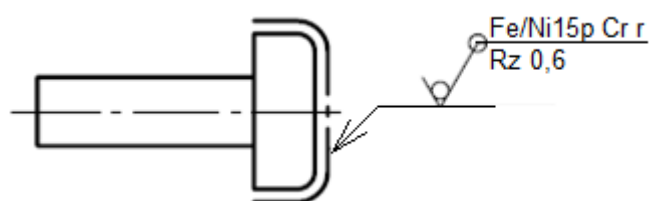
Úprava povrchu špeciálnym mechanickým spracovaním
